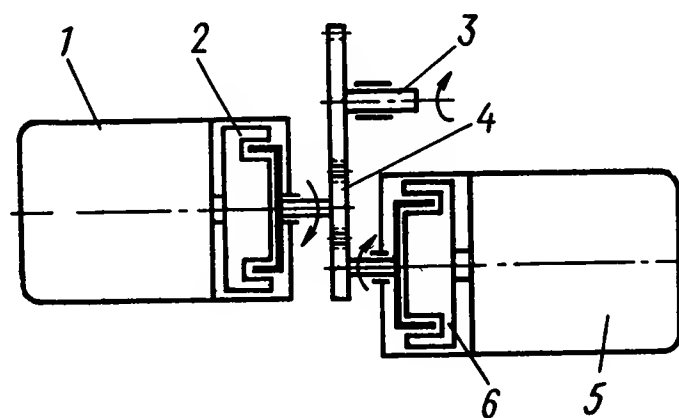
Кинематическая схема исполнительного устройства с двумя электродвигателями:
